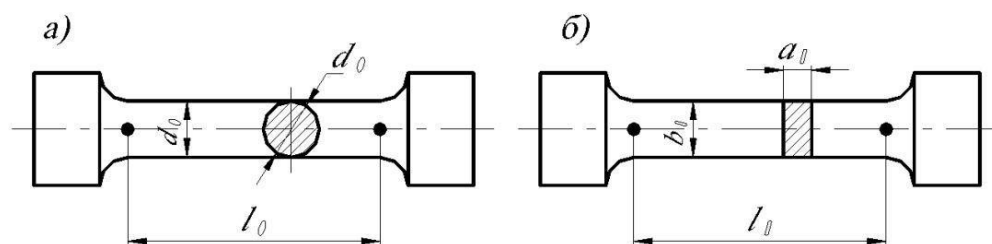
образцы для испытаний на разрыв: а – круглый; б – плоский
